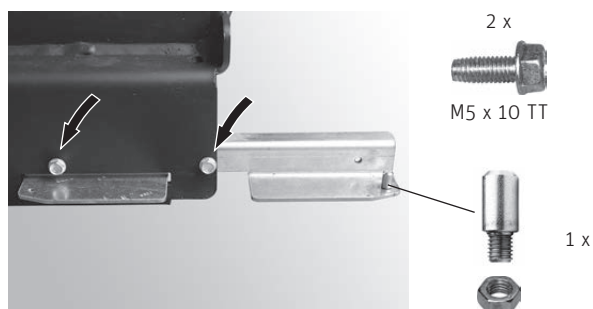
Montare il cardine per la porta di contenimento a sinistra o a destra
